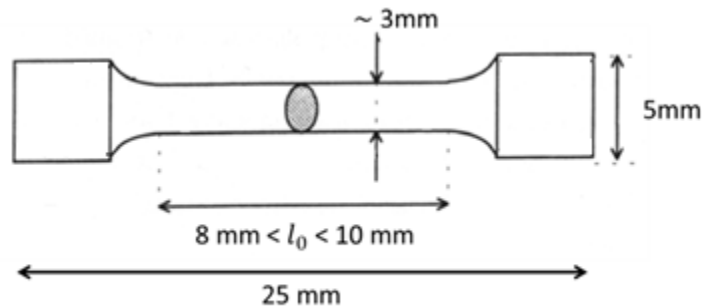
dimension des éprouvettes frittées dans la Gleeble après usinage.
